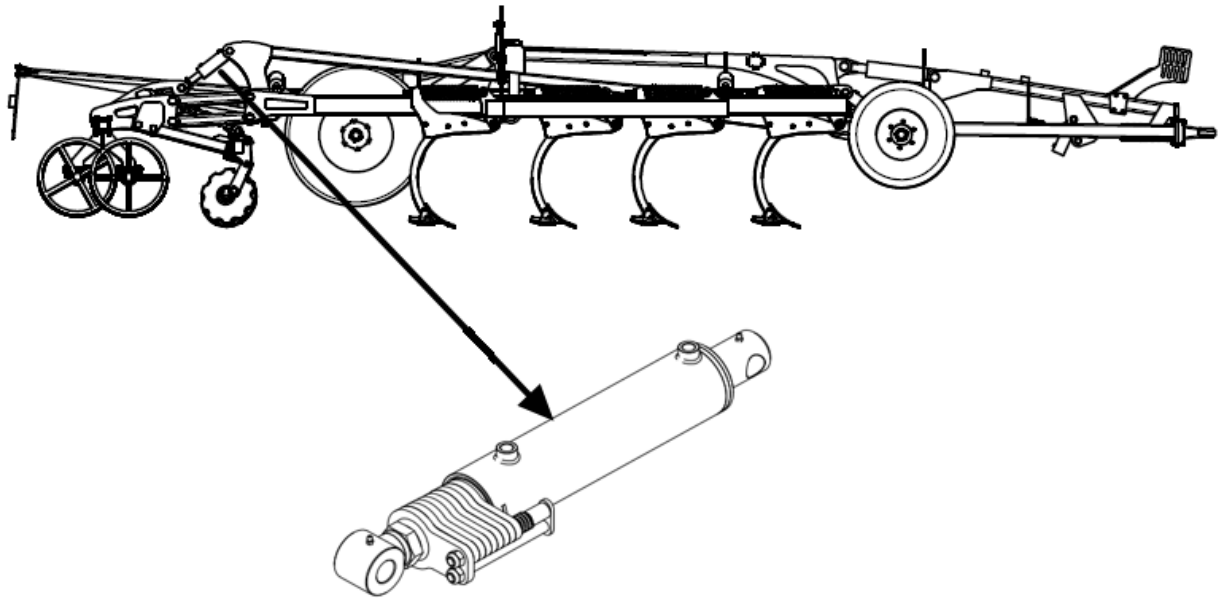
Vérin avec des cliquets fixés à la tige du piston pour régler la profondeur de travail.
